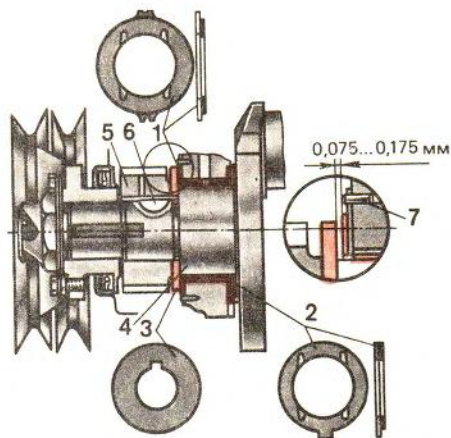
Передняя часть коленчатого вала двигателя ЗМЗ-24Д:
